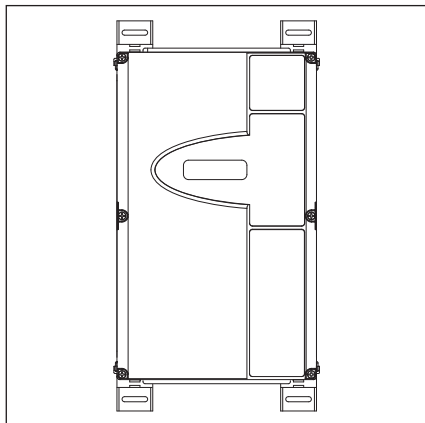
Корпус блока управления с вертикально закрепленными монтажными опорами
